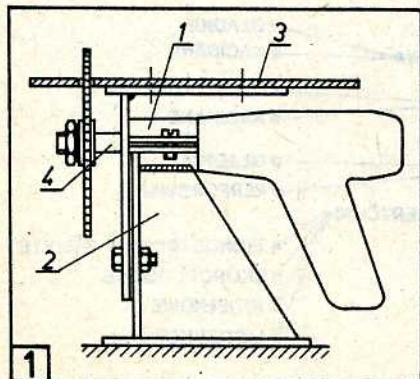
Pilarka: 1 – pierścień zaciskowy; 2 – podstawa; 3 – stolik; 4 – łącznik
